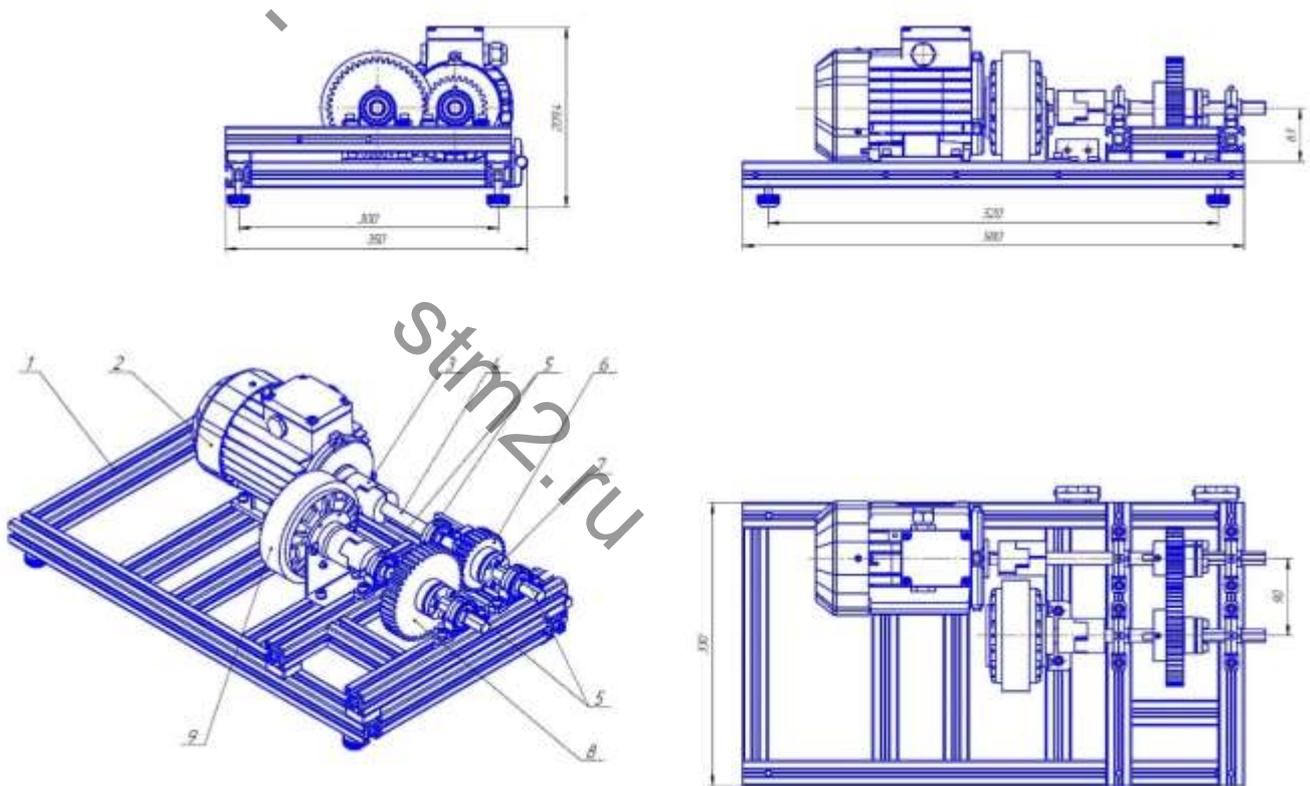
Чертеж стенда в конфигурации с зубчатыми колесами
